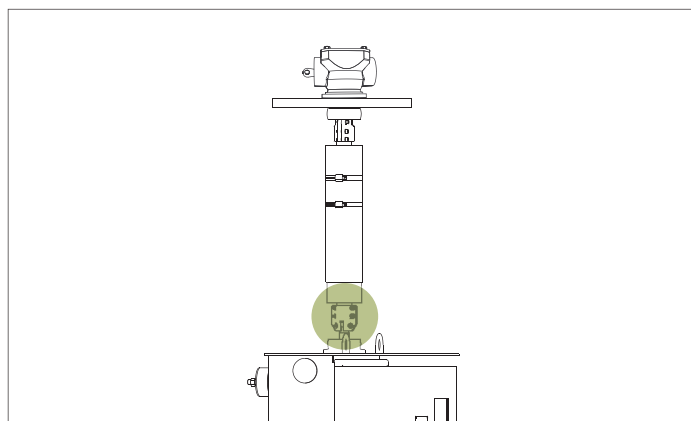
Присоединение вала квадратного сечения к моторному приводному механизму
